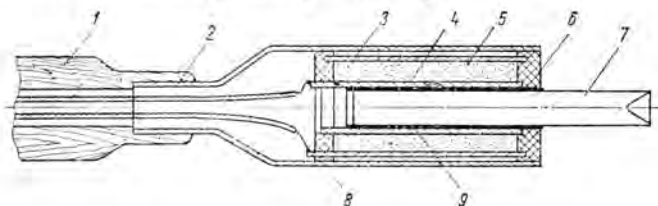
Конструкция паяльника, рассчитанного на питание от электросети: 1 — ручка; 2 — корпус; 3 и 4 — электроды нагревателя; 5 — графитопесчаная смесь; 6 и 8 — изоляторы; 7 — паяющий стержень; 9 — прокладка слюдяная.
